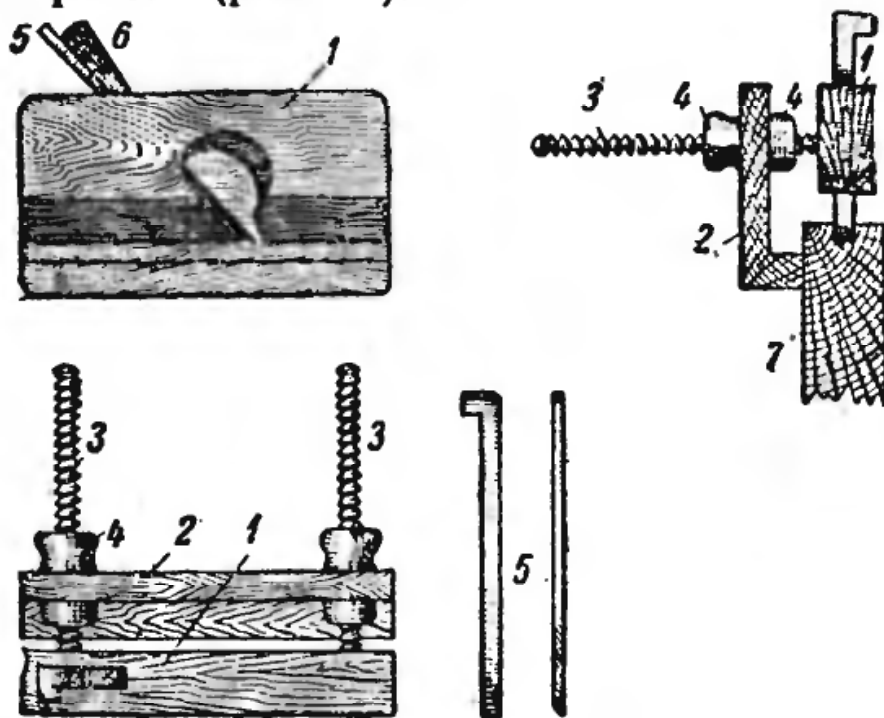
Шпунтубель: 1 — колодка, длина 240—250 мм; 2 — упор — переставная колодка; 3 — винты направляющие; 4 — контргайки, длина 180—200 мм, ширина — по размеру отбираемого шпунта (паза); 5 — железка; 6 — клин; 7 — обрабатываемая деталь.
